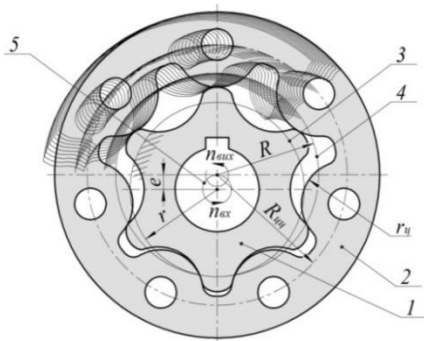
Схема обкату цівкового колеса навколо нерухомого сателіта: 1 – сателіт; 2 – цівкове колесо; 3 – центроїда сателіта; 4 – центроїда цівкового колеса; 5 – траєкторія, описана центром колеса в процесі обкату
